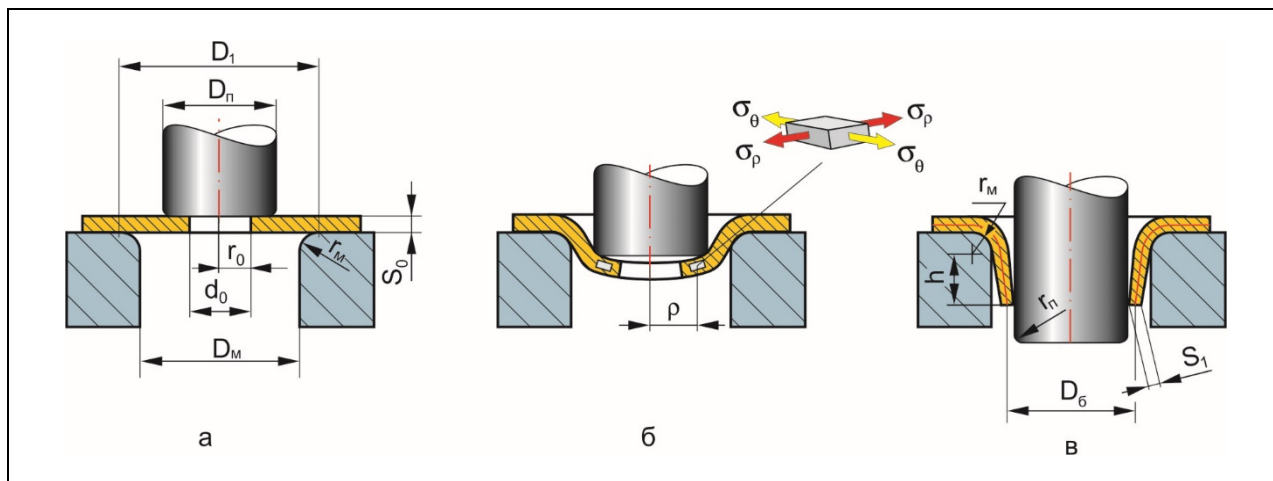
Схема формоизменения заготовки в процессе отбортовки
